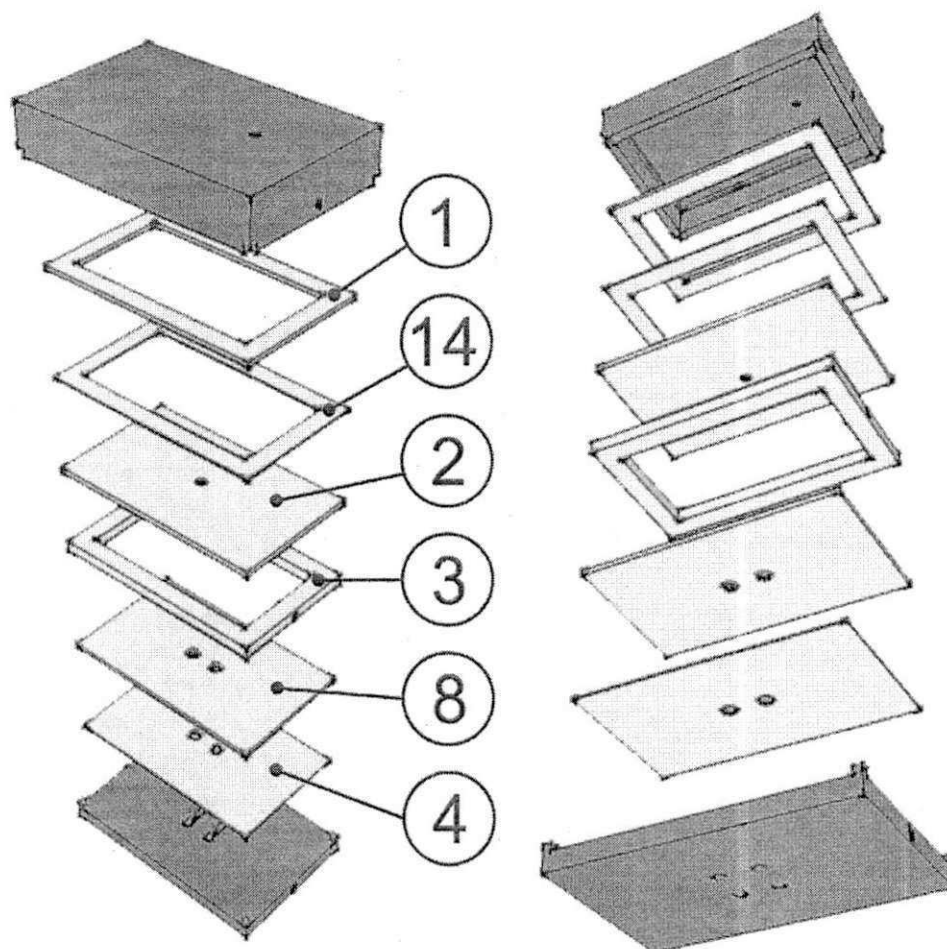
Montagem explodida da microválvula (com componentes adicionais da tampa): vistas superior e inferior
